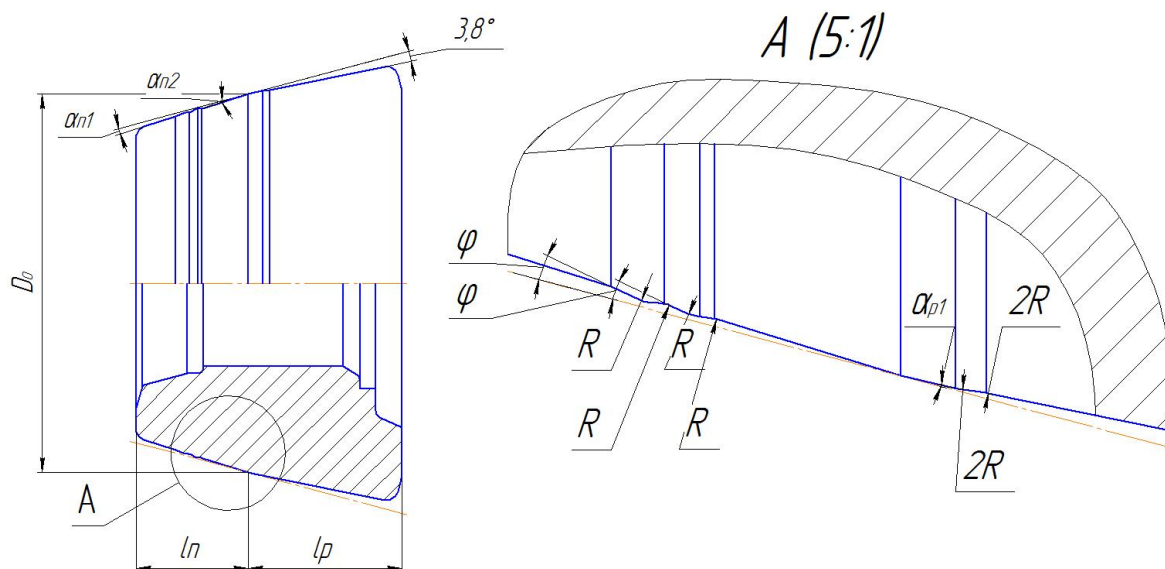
Схема опытной кольцевой калибровки валков прошивного стана
